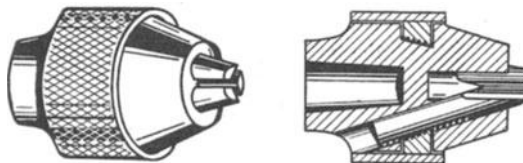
Dreibacken-Bohrfutter mit Spiraling (Spitzgewinde).
